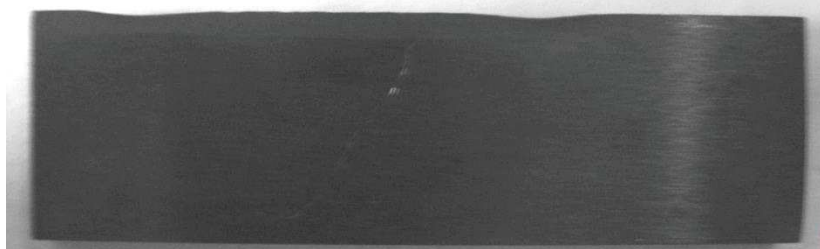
Фото резца обрабатывающего кромки ДСтП
